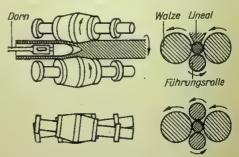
Schrägwalzverfahren nach Mannesmann
